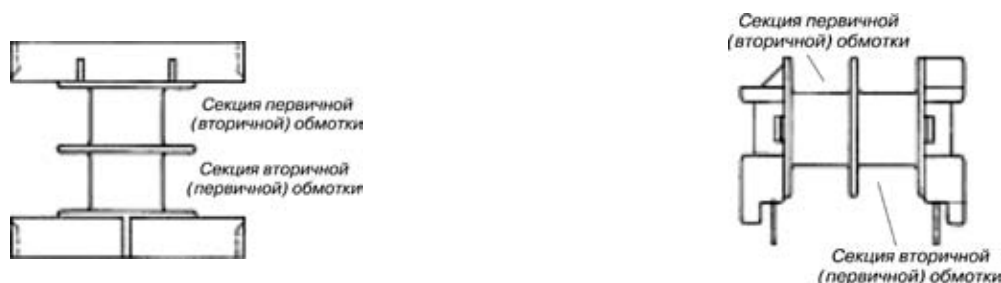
Расщепленный двухсекционный каркас для изготовления магнитно связанного дросселя: а – вид сверху; б – вид сбоку
